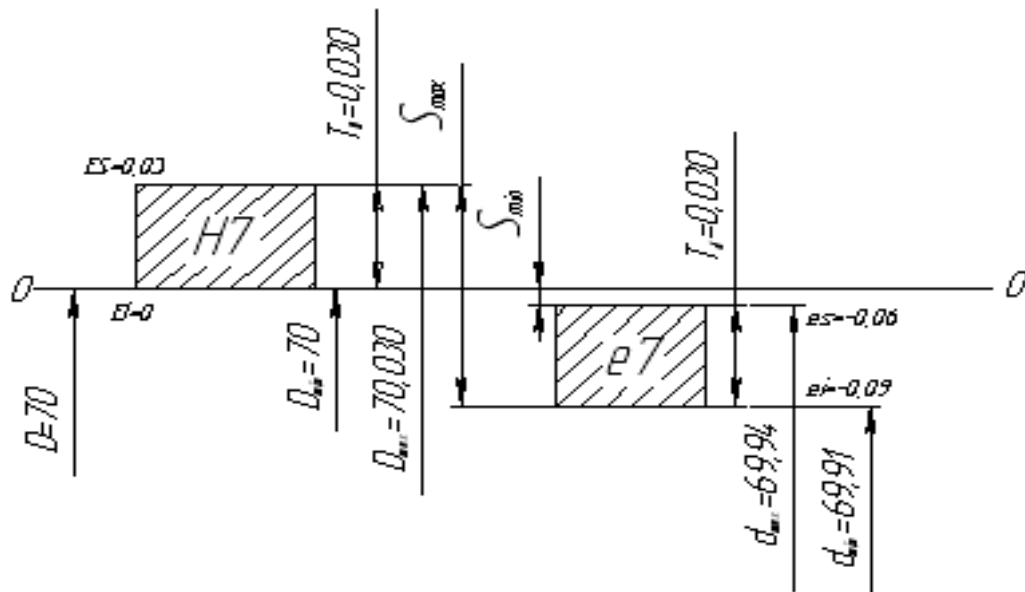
Схема розташування полів допусків для посадки з зазором
